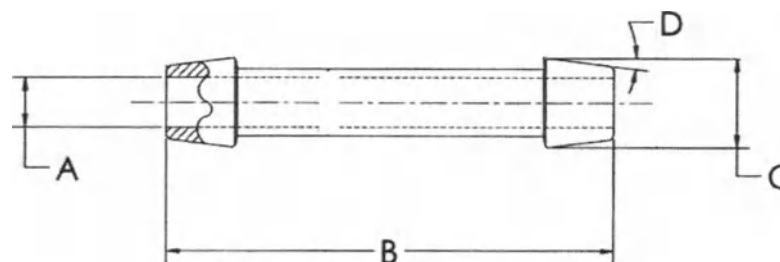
Соединитель из нержавеющей стали, общий вид / Figure 12 – Stainless Steel Connector, general view
